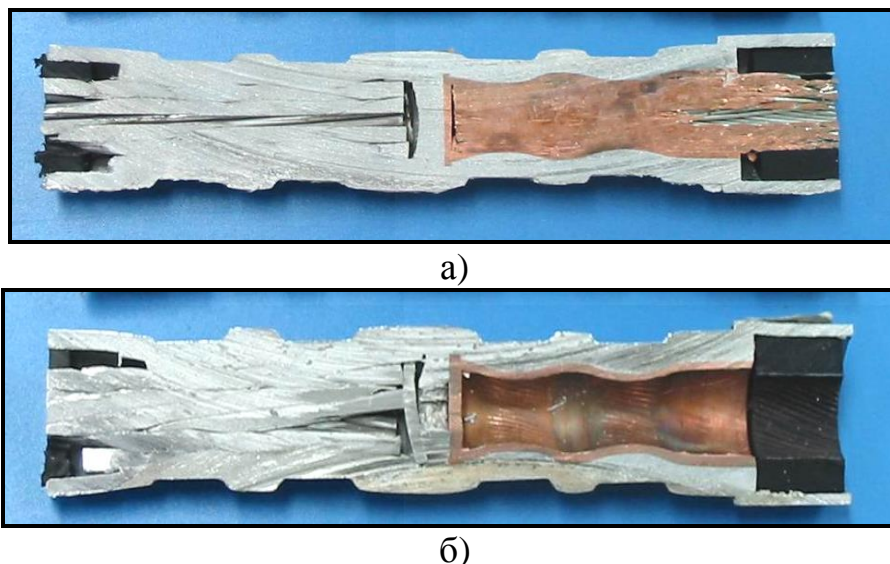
Макрошліфи біметалевих гілз, виготовлених за комбінованою технологією зварювання вибухом + зварювання тертям: а) - біметалічна вставка і трубка, отримані методом зварювання вибухом і з'єднані з алюмінієвою трубкою зварюванням тертям; б) – вставка, виготовлена з двох окремих пластин, біметалічна трубка, отримана методом зварювання вибухом і з'єднана з алюмінієвою трубкою зварюванням тертям
